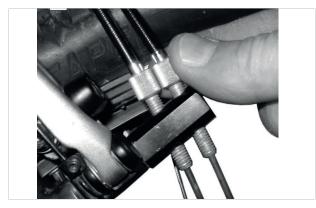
ROHLOFF-Naben Versionen mit interner Schaltansteuerung haben die Zugeinsteller am Zuggegenhalter
